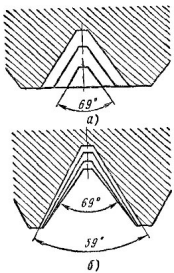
Нарезание наружной метрической резьбы по металлу
